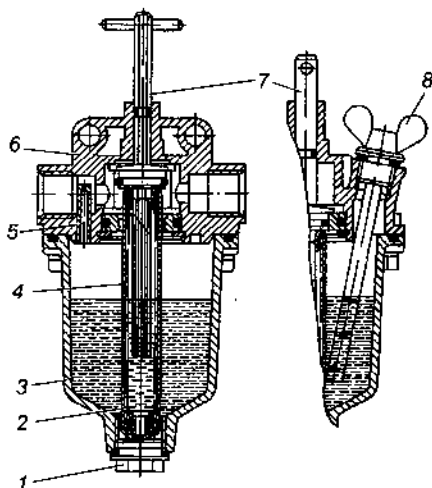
Предохранитель от замерзания: 1 — пробка; 2 — пружина; 3 — крышка; 4 — фитиль; 5 — жиклер; 6 — корпус; 7 — шток; 8 — пробка с указателем уровня спирта
